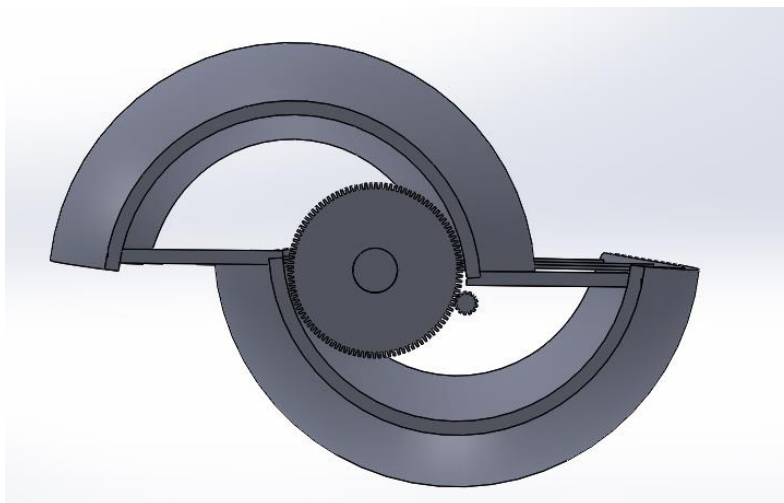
Vista superior del acoplamiento de engranes. Diseñada con SolidWorks®.
